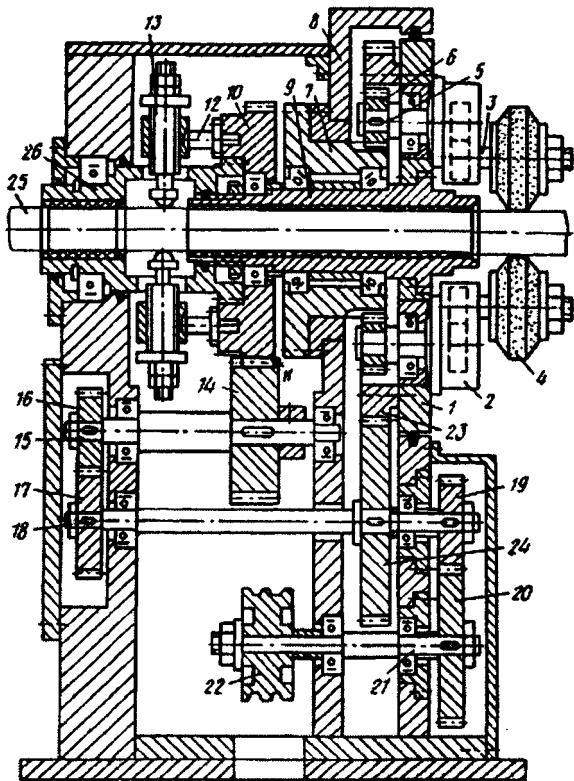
Схема реализации способа совмещенной обработки иглофрезерованием и ППД: 1 – корпус, 2 – качающийся редуктор, 3 – выходной вал, 4 – иглофреза, 5 – приводной вал, 6 – шестерня, 7 – шестерня, 8 – кожух, 9 – втулка, 10 – диск, 11 – зубчатый венец, 12 – держатель, 13 – деформирующий элемент, 14 – шестерня, 15 – вал, 16 – сменная шестерня, 17 – сменная шестерня, 18 – вал, 19 – сменная шестерня, 20 – вал, 21 – вал, 22 – шкив, 23 – шестерня, 24 – шестерня. 25 – обрабатываемая заготовка, 26 – втулка
